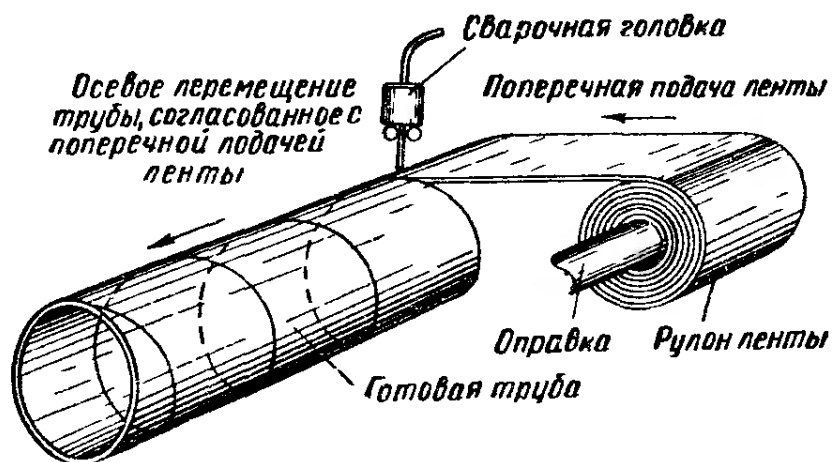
Схема процесса сварки из ленты труб со спиральным швом
